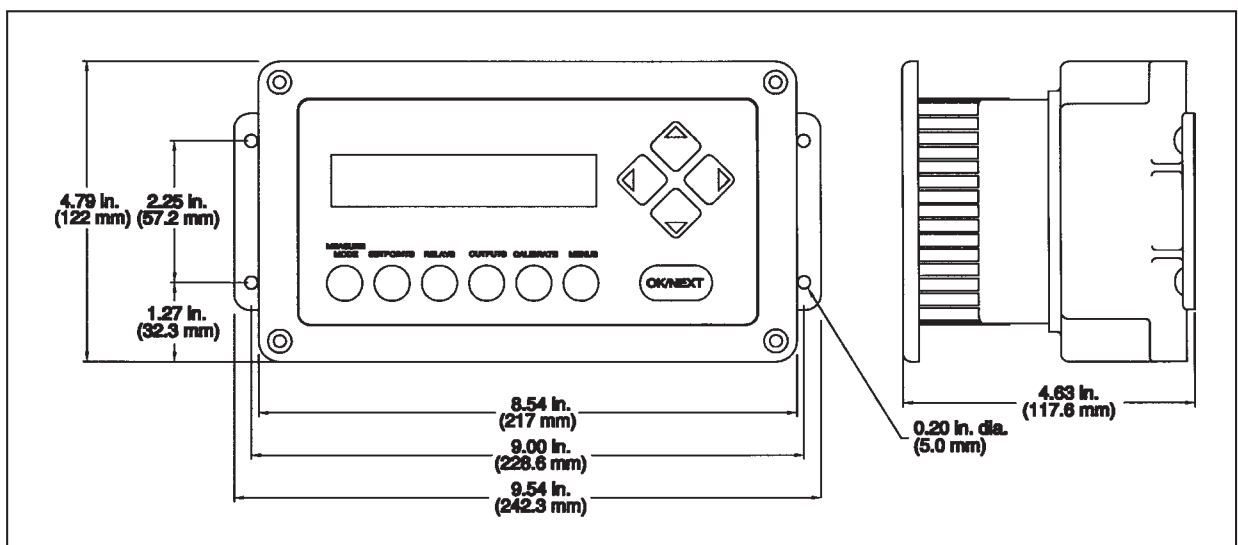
Dimensões para Montagem em Parede (com tampa traseira acessória instalada)
